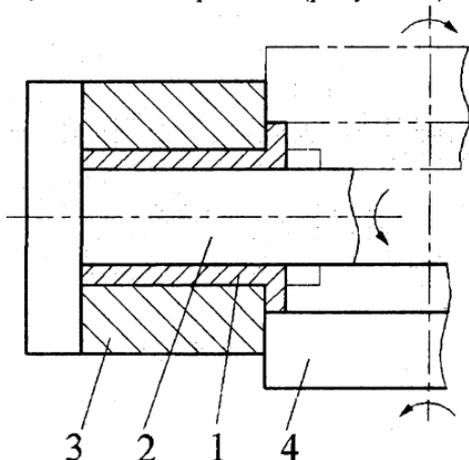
Схема торцевой раскатки заготовок при силовом воздействии деформирующими валками: 1 – заготовка; 2 – оправка; 3 – обойма; 4 – деформирующий валок (валки)
